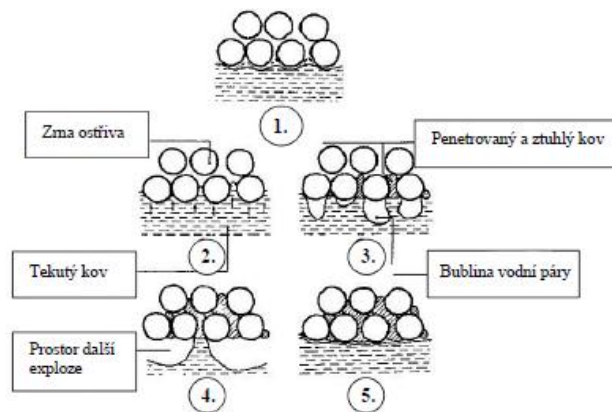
Příklad výronku kovu představující hlubokou přípečeninu [26].
